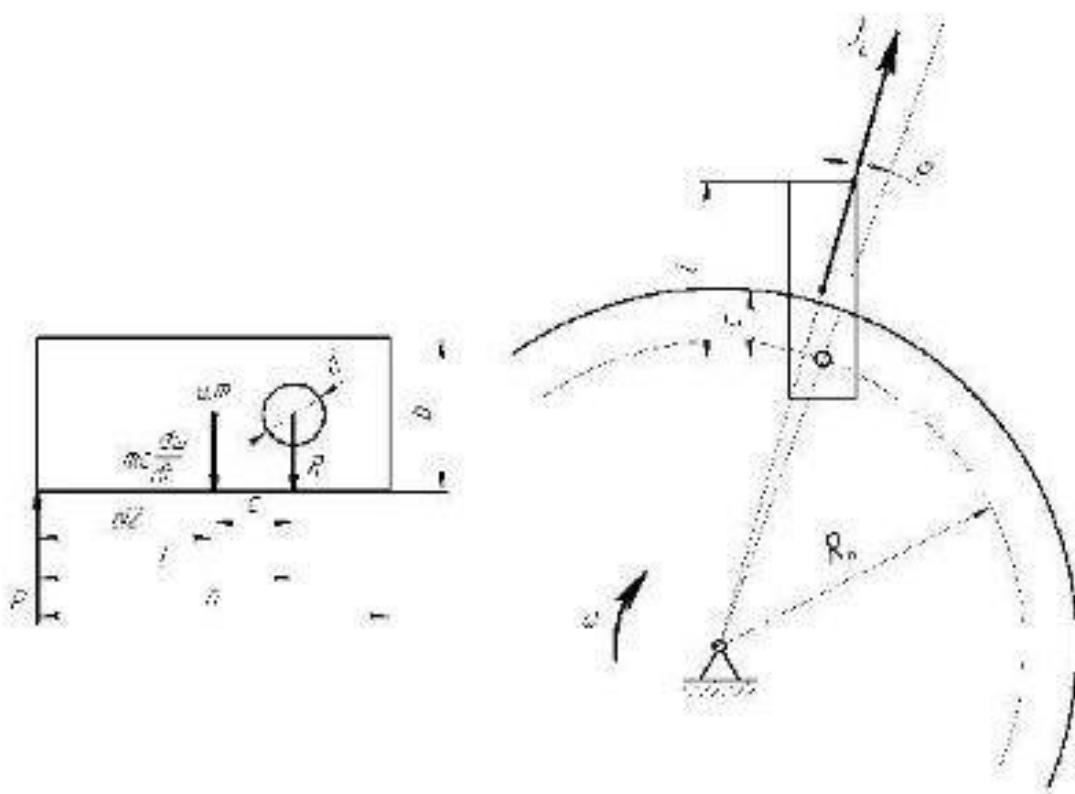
Схема для определения размеров молотка дробилки
